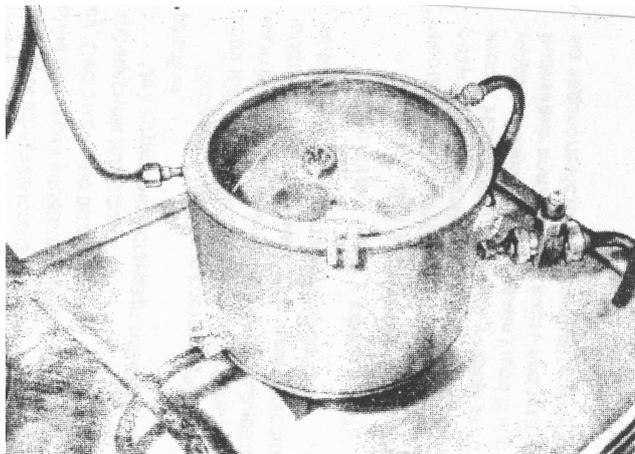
Рабочая камера установки (с открытой крышкой) с расположенными на сетчатой подставке эпиламируемыми изделиями
